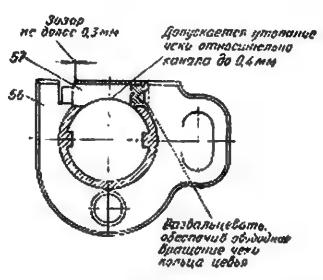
Постановка чеки кольца цевья: 66 — кольцо цевья; 57 — чека кольца цевья
